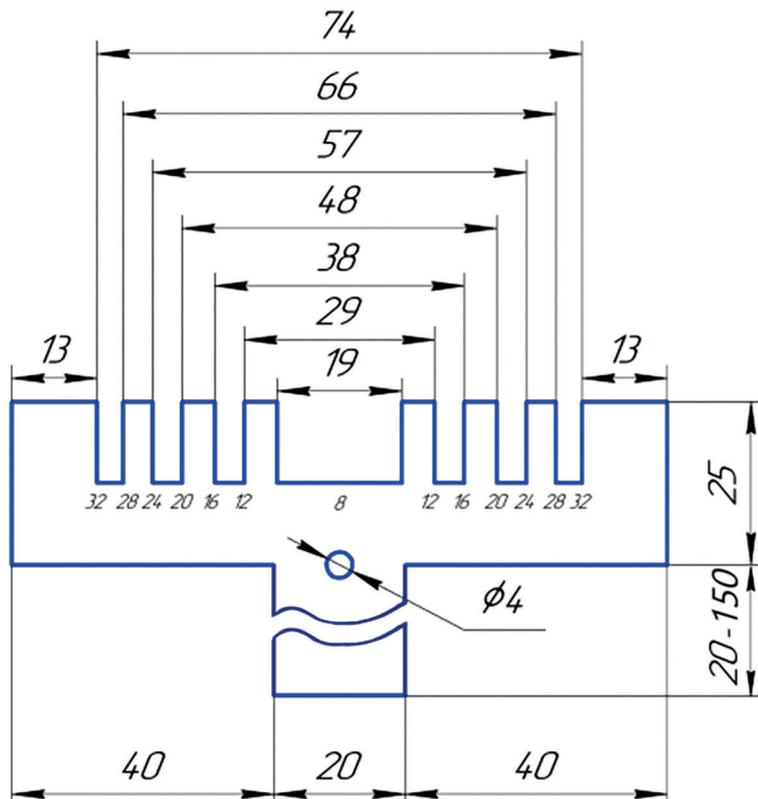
СХЕМА ПРЕДЛАГАЕМОГО ИНСТРУМЕНТА
